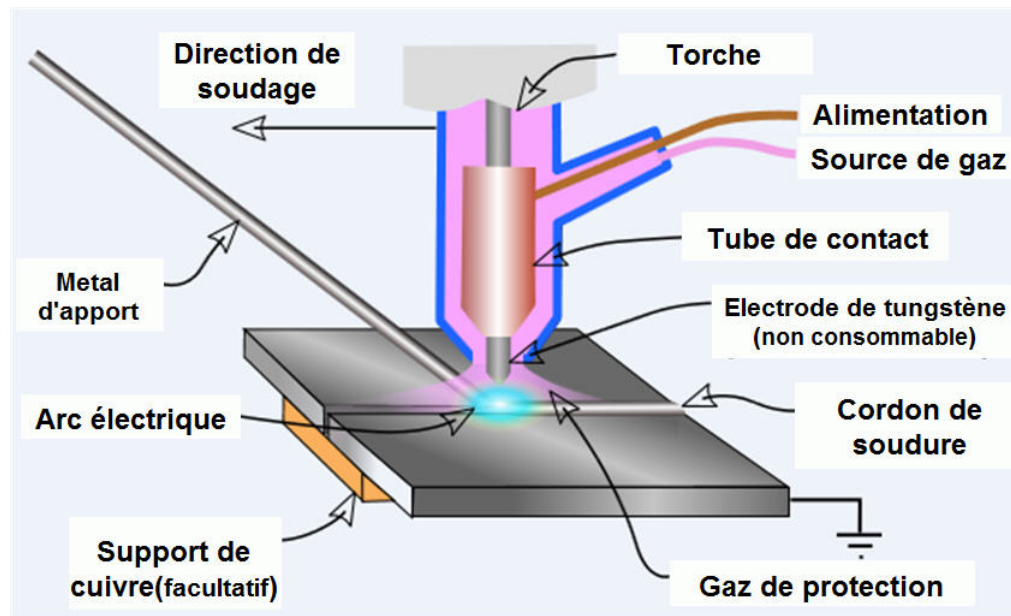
Schéma de principe du soudage TIG.
